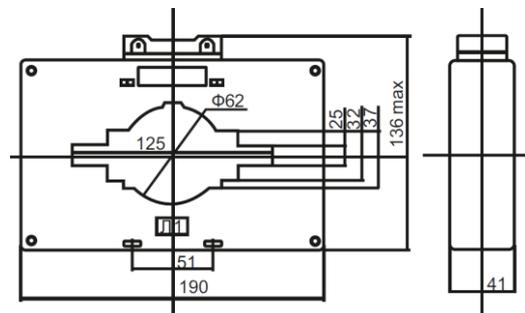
Габаритные и установочные размеры трансформаторов тока ТШП-0,66-120
